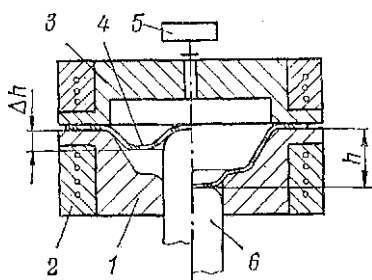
Схема пневмотермической формовки [106]: 1 — матрица, 2 — нагревательные элементы, 3 — крышка, 4 — деформируемая заготовка, 5 — пневмосистема избыточного давления, 6 — устройство поддержки
